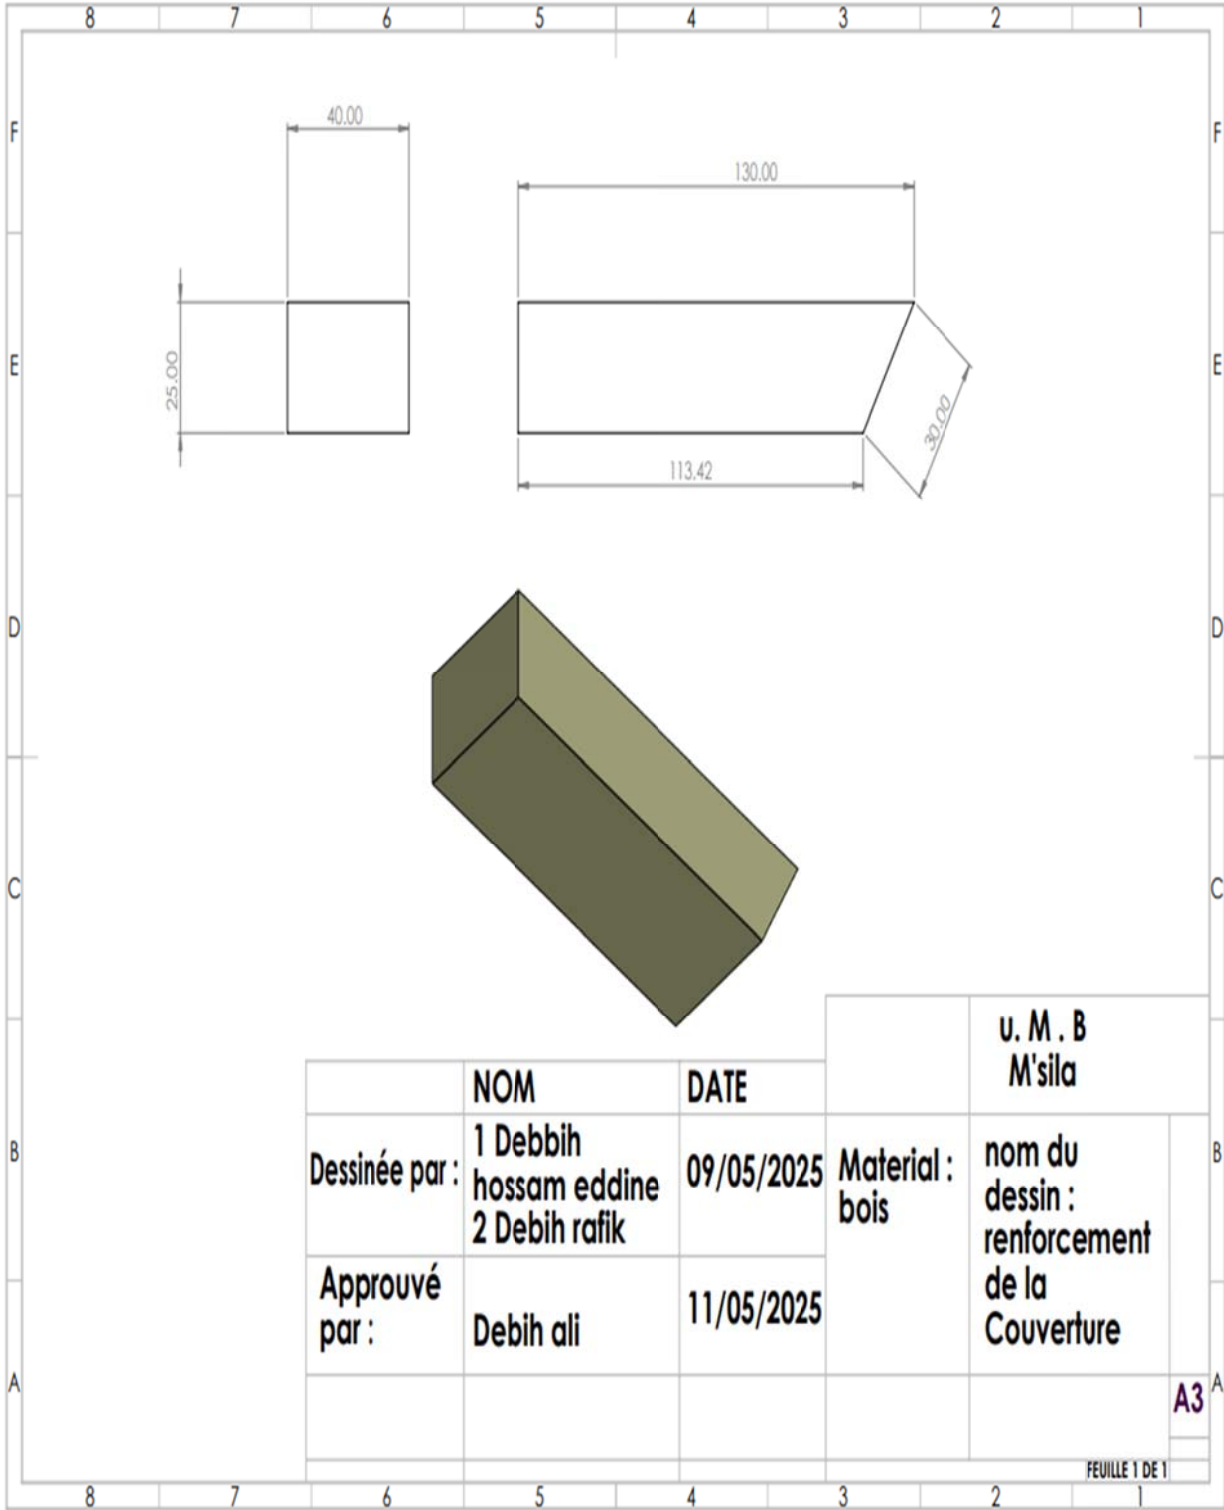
Dessin Couverture de poste a souder par points.
